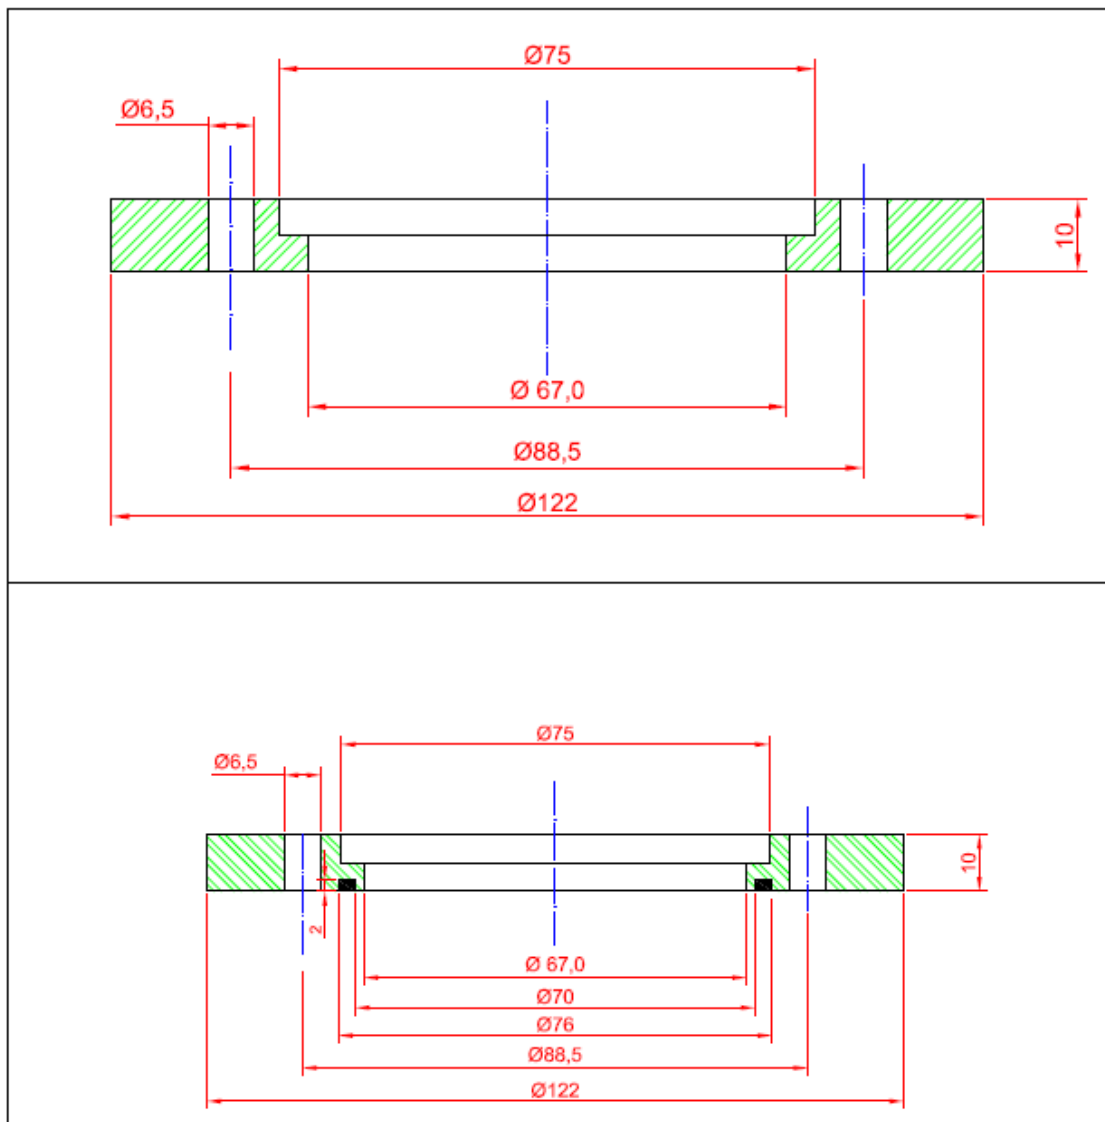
Flange para usinagem-CAP Conexão ao Sistema de Vácuo
